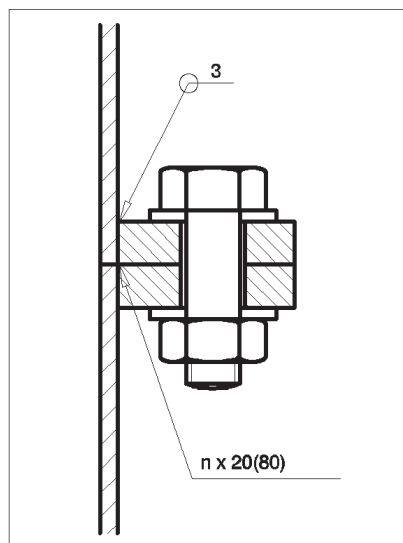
Flanschverbindung mit Flansche, geschweißt.
